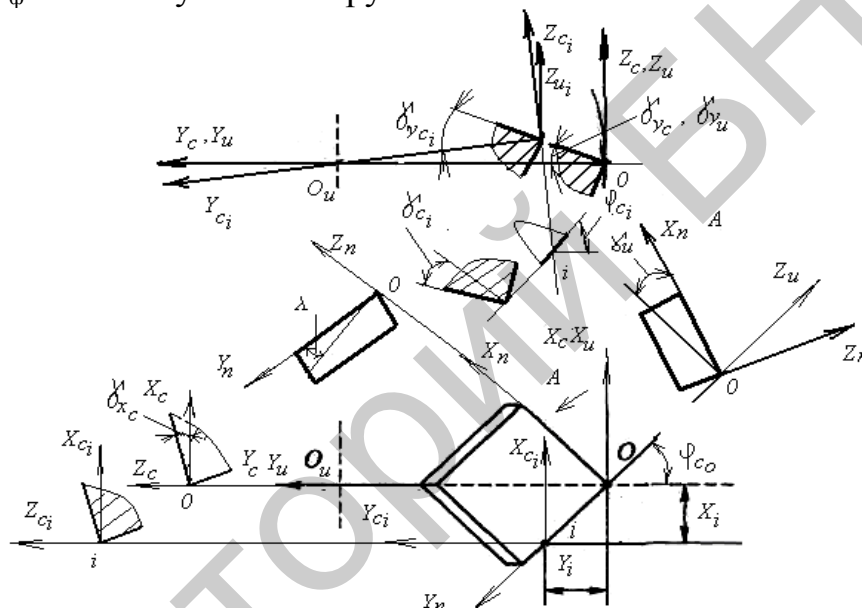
Схема к расчету статических углов сборных инструментов с главным вращательным движением
